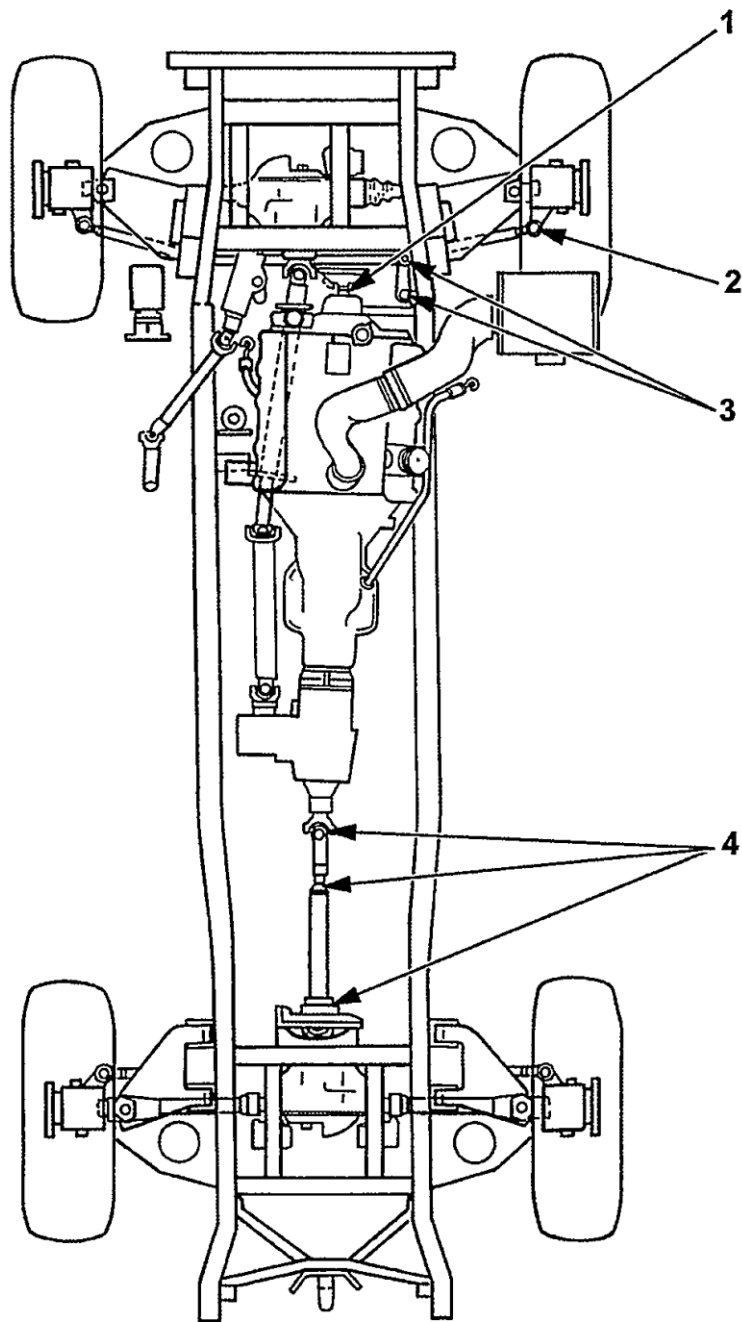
Точки змащування — вентилятор з редукторним приводом, поперечна кермова тяга, маятниковий важіль і задній карданний вал.
